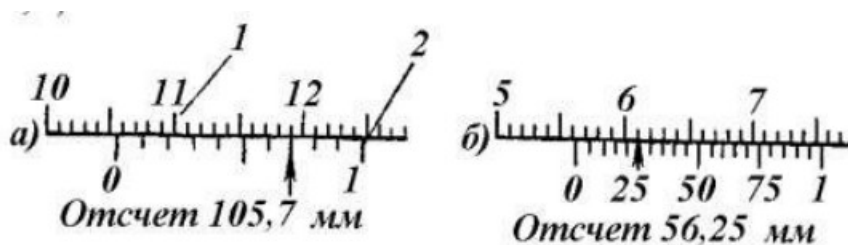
Примеры отсчета размеров по нониусу штангенинструмента: 1 – основная шкала; 2 – шкала нониуса
